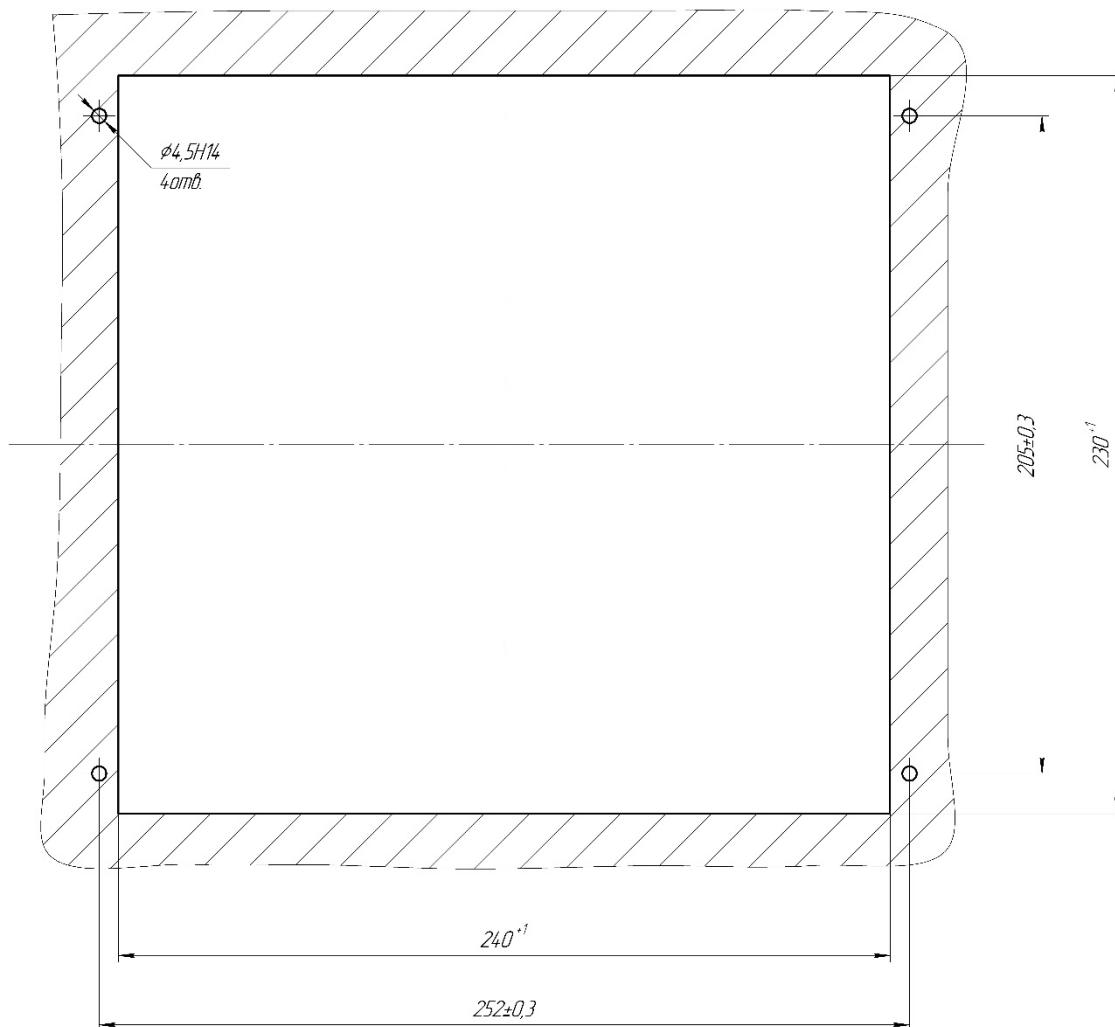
Габаритные размеры окна и крепежных отверстий для установки устройств РЗЛ-05.АХ, РЗЛ-05.А1Х, РЗЛ-05.А2Х
